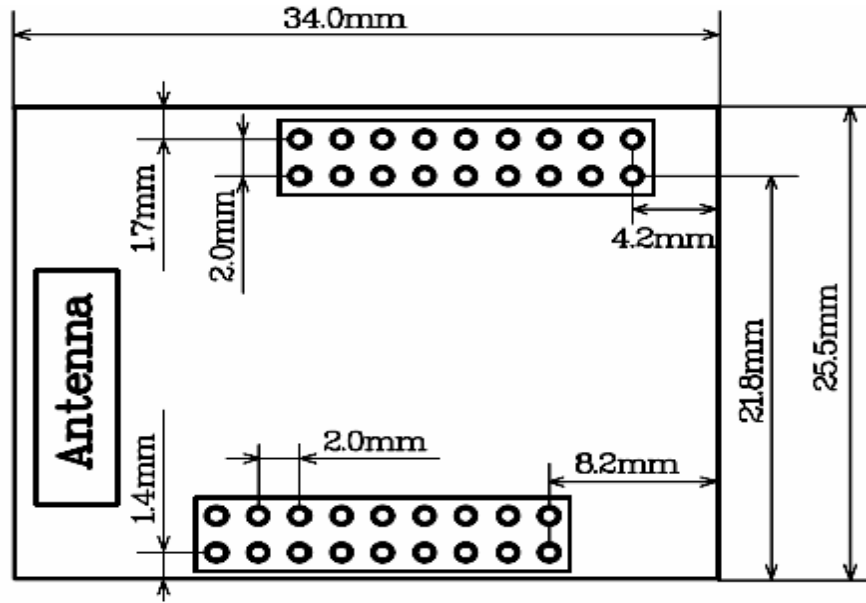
GC-06 (GC-04-DIP) 外形尺寸 (顶视图)
